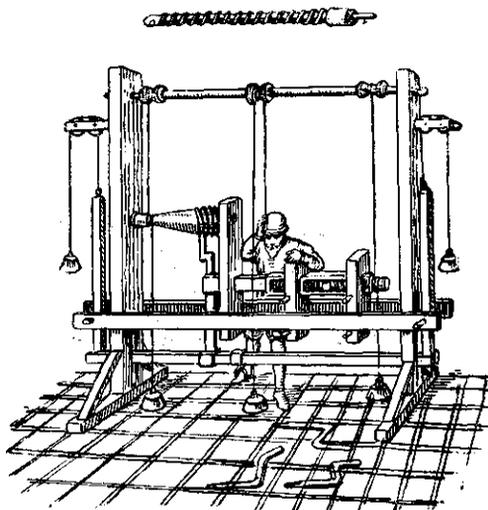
Токарно-винторезный станок Жака Бессона с копиром для резьбы и ножным приводом.
